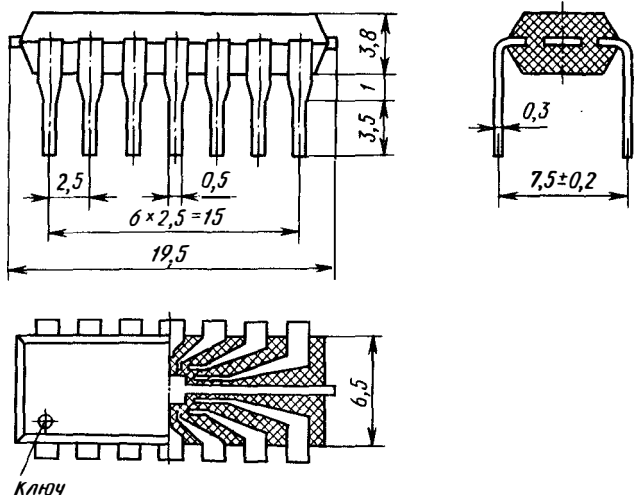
Монолитный полимерный корпус ИС типа 201.14-1
